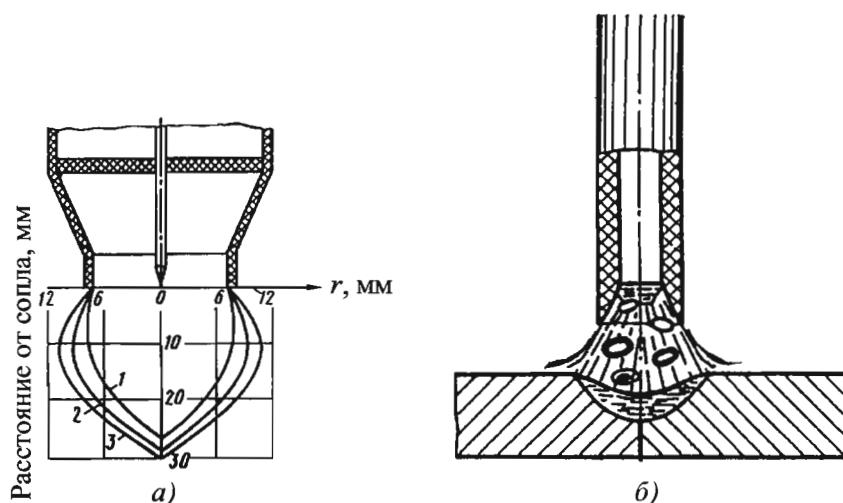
Схемы струйной газовой защиты металла при дуговой сварке в газах (а) и электродом с покрытием (б):
